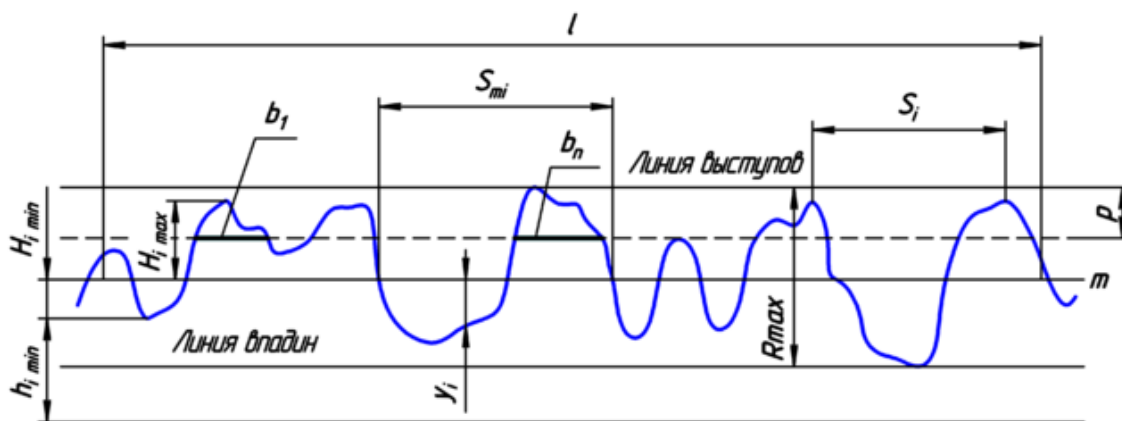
Нормальный профиль и параметры шероховатости поверхности.
